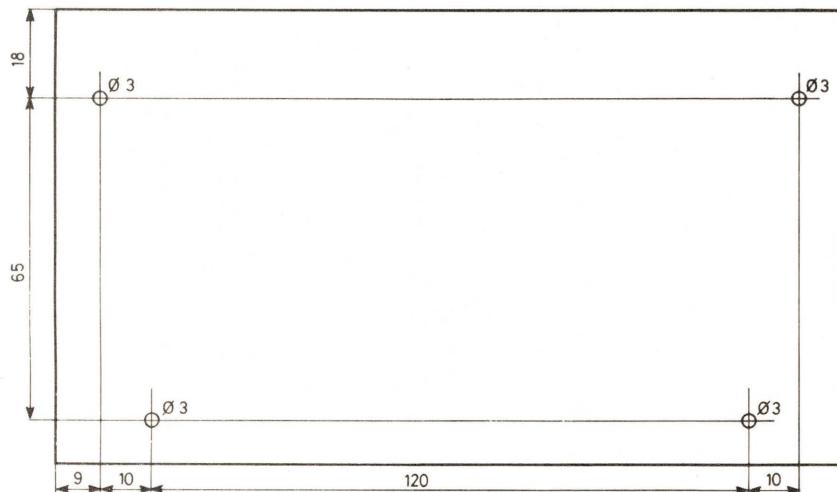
et 6. – Plan de perçage du fond du boîtier Teko P/3 et plan de câblage général du montage pourvu de dominos de raccordement.
